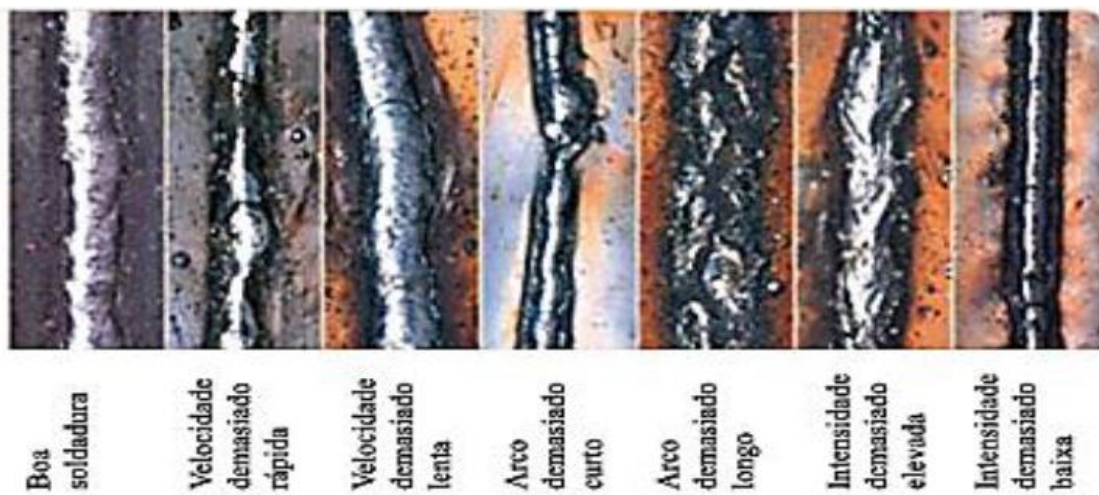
Forma dos cordões de soldadura em função dos erros de regulação eventualmente cometidos sobre cada um dos parâmetros de soldadura no processo de Eléctrodo revestido (Silva F. J., 2016)
